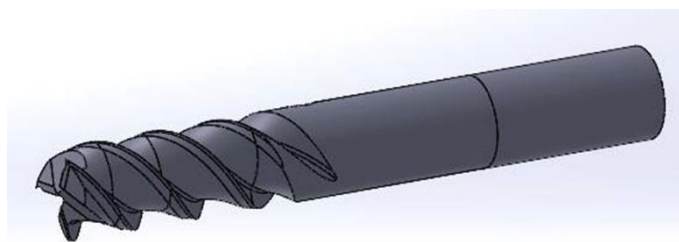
3D-модель кінцевої фрези в SolidWorks
